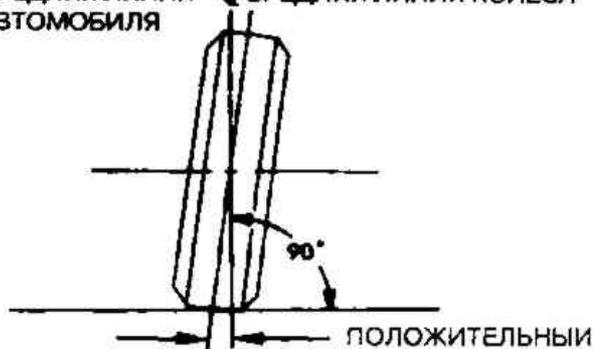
Схема измерения развала колес (Разд. 23)
